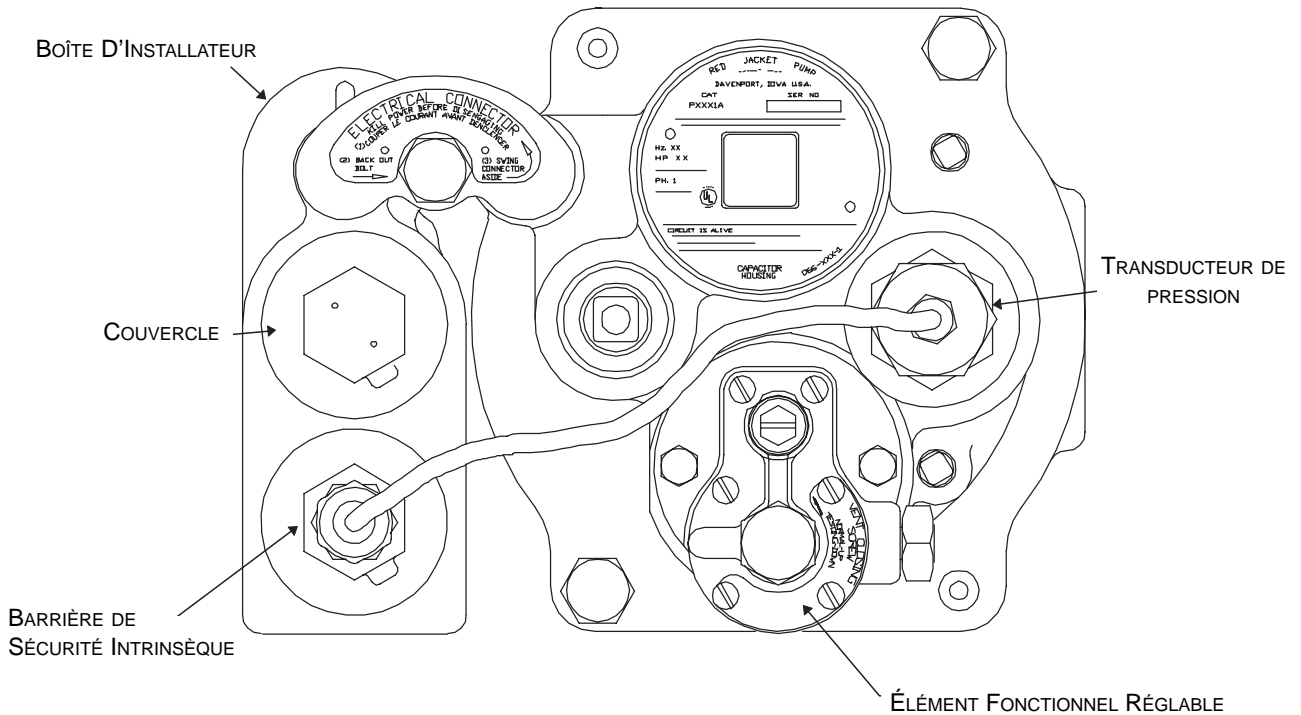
VUE DE DESSUS DU PRESSE-ÉTOUPE
